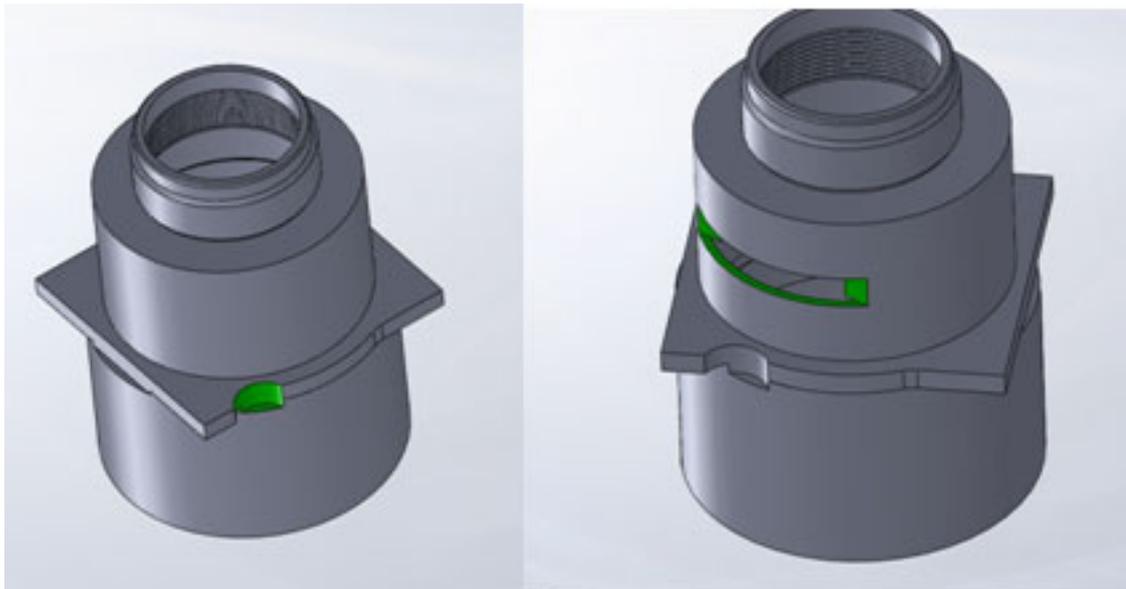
Трехмерные эскизы для фрезерных операций с визуальным изображением обрабатываемых поверхностей
